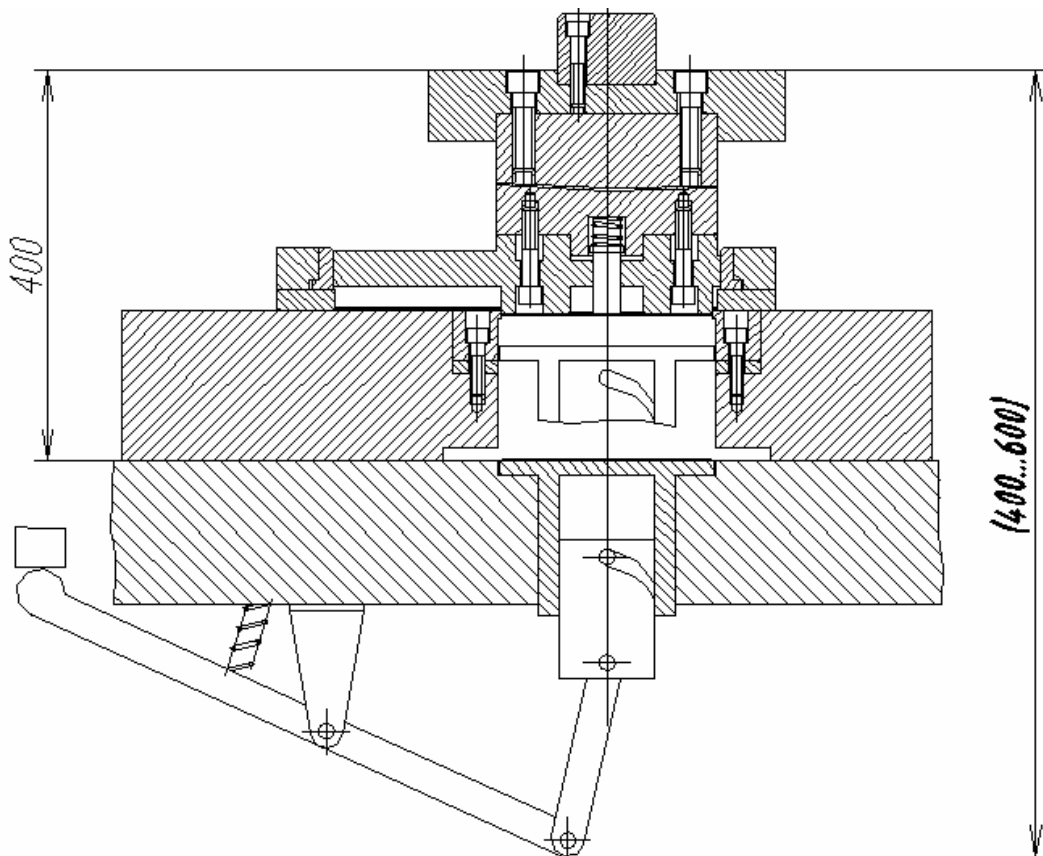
Фронтальный разрез штампа на столе пресса и устройство для переориентации заготовки
